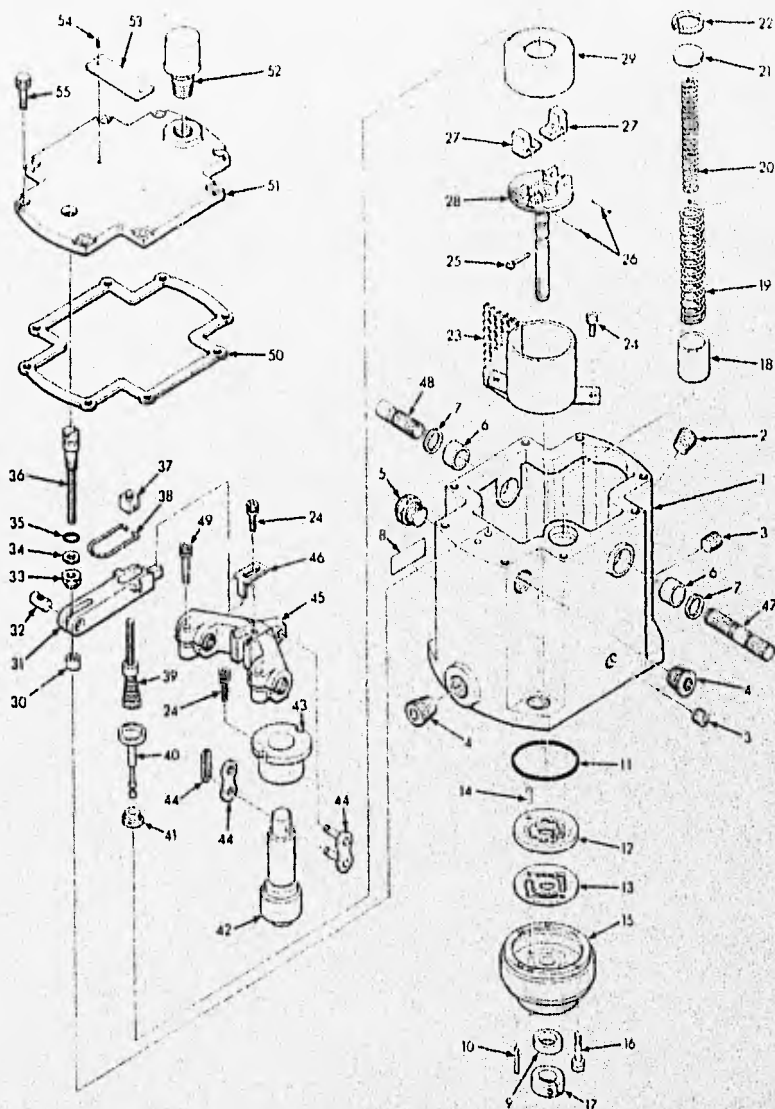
VISTA EN EXPLOSION DE LOS COMPONENTES DEL GOVERNADOR.
